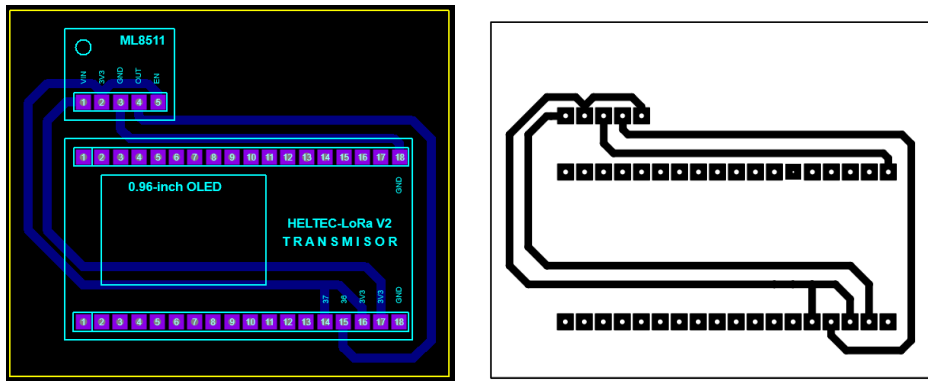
Visualización del diseño PCB de la placa transmisora
